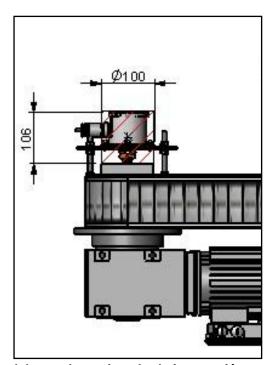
Dimensiones del encoder y ejemplo de integración con la cinta transportadora
